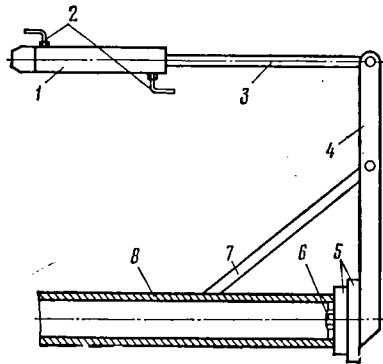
Схема заглушки для открытия и закрытия трубопроводов при подаче минерального порошка:
